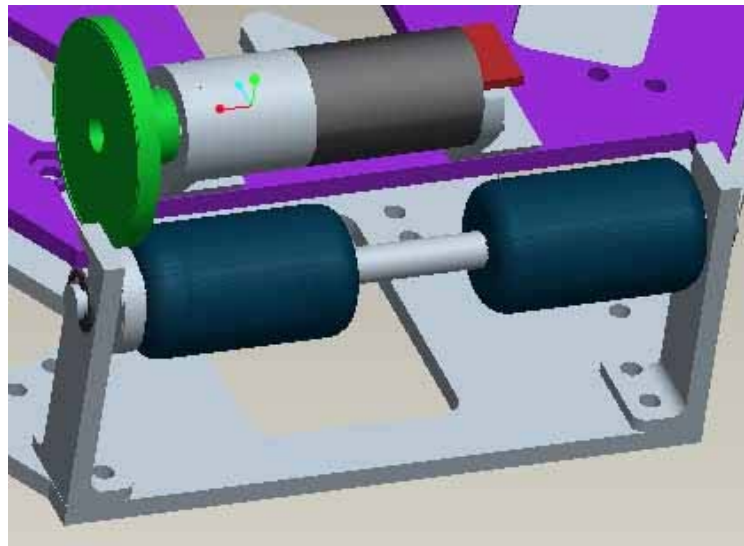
Ensamble del Sistema de Control de Bola
